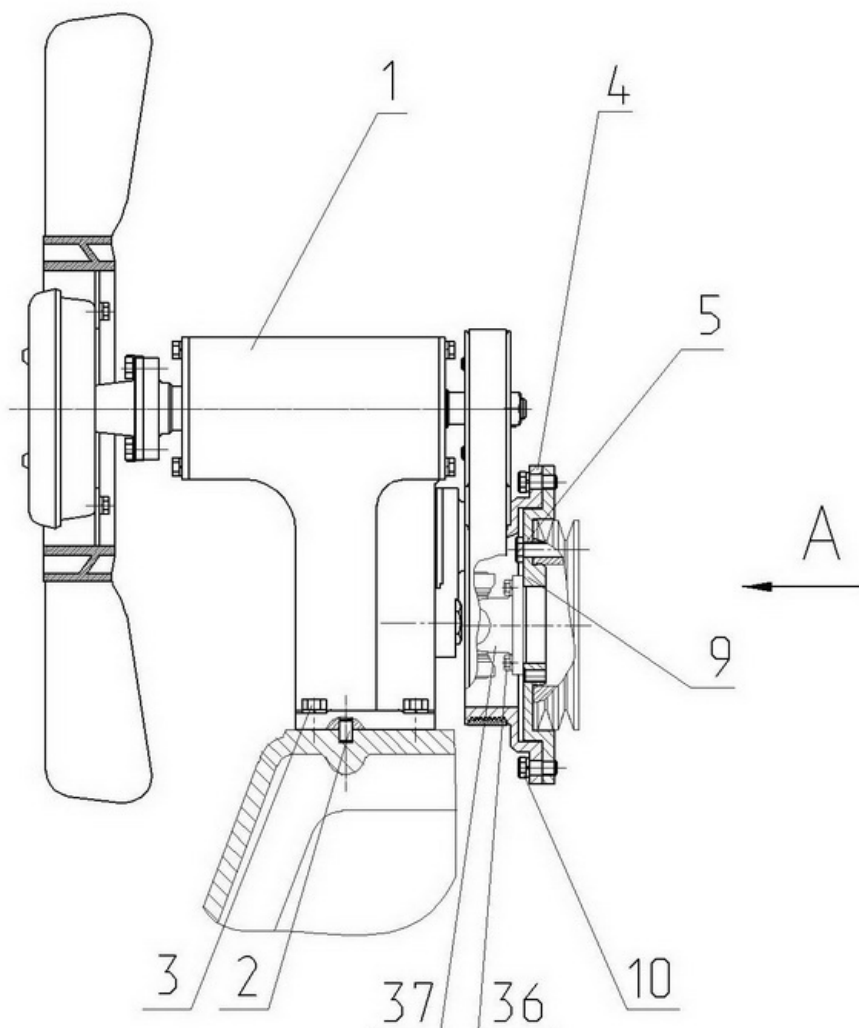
Привод вентилятора на двигателе DEUTZ.
